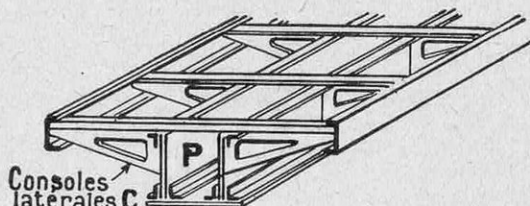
COUPE DU CHASSIS DE LA FIGURE 1
